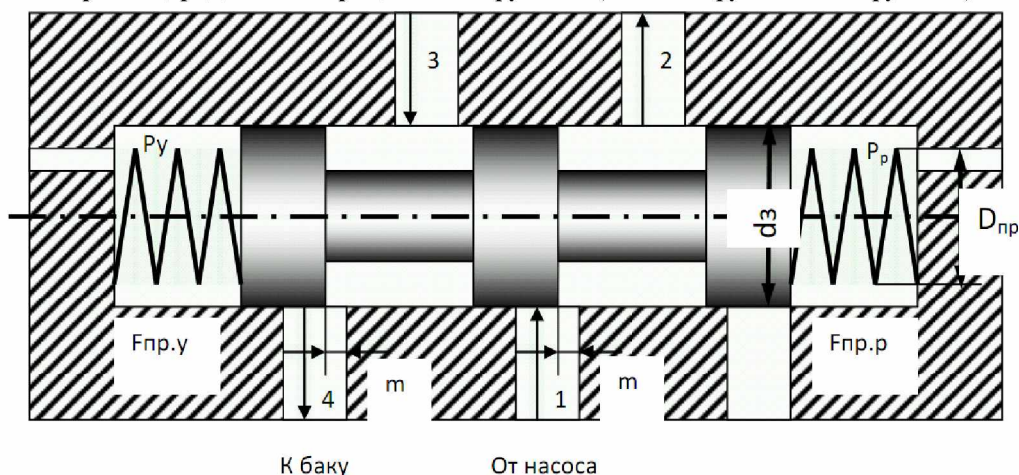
Расчетная схема золотника регулятора: 1- напорный канал; 2 – канал идущий к двигателю подачи; 3- канал идущий от двигателя подачи; 4- сливной канал; P_y - канал управления от гидроцилиндра; P_p - канал управления от гидромотора дискового инструмента.
